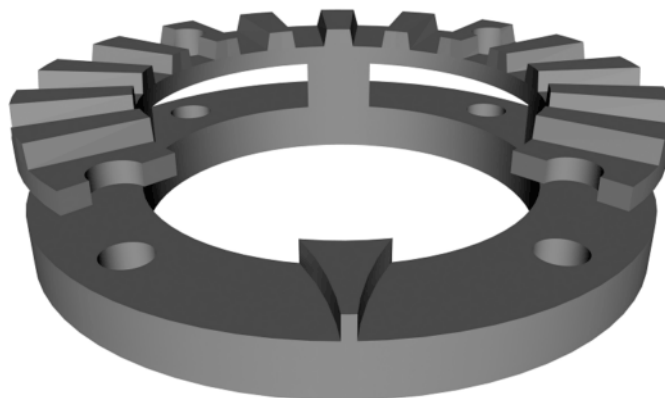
Правая полушестерня резцедержателя, используемая в качестве упругого элемента датчика
